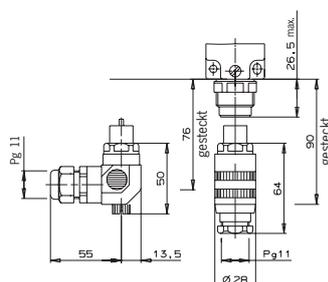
Maßzeichnung NZ2VZ-5... mit Steckverbinder SR6
